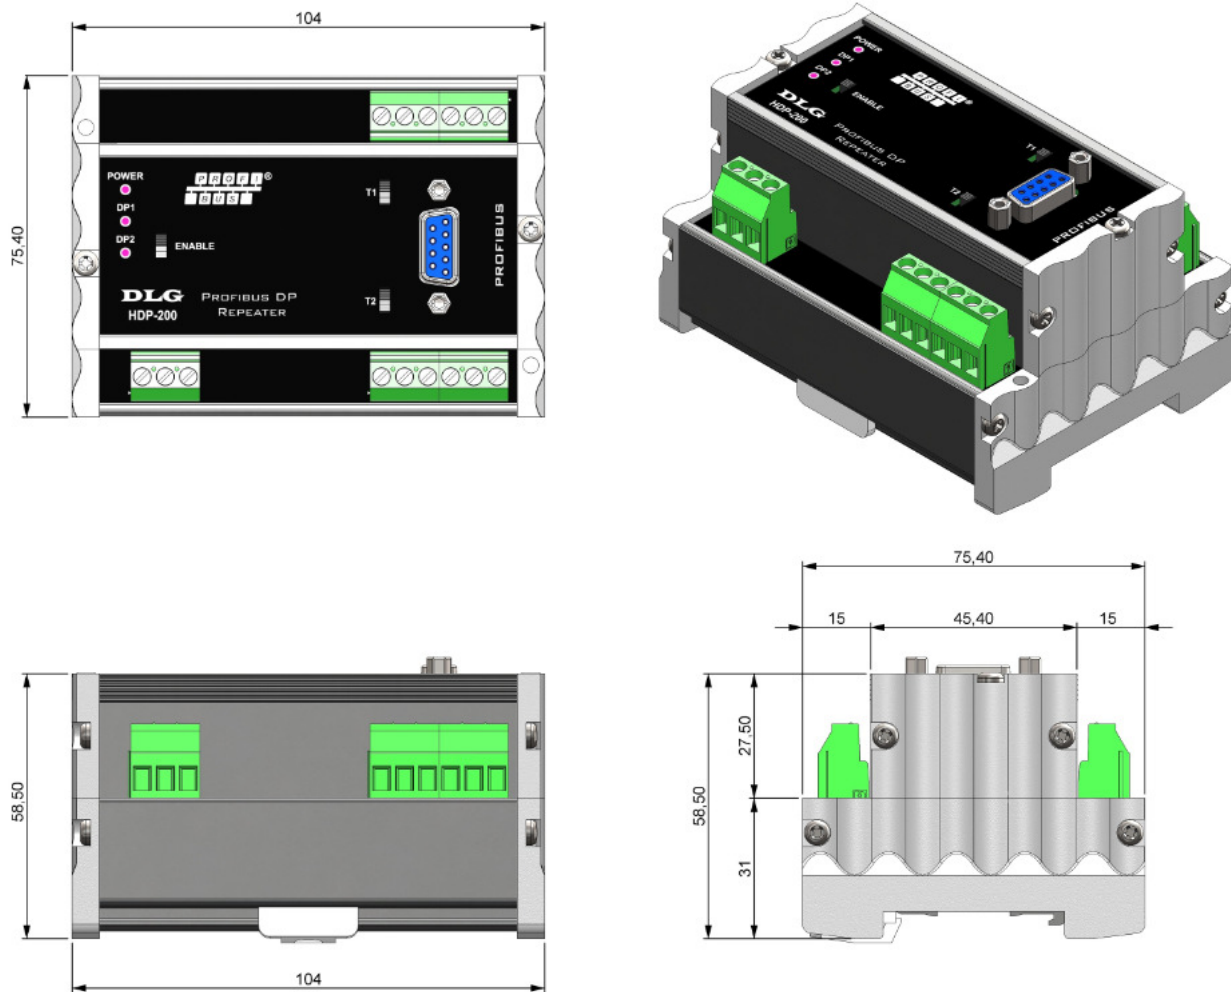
Dimensionamento para montagem (cotas em milímetros)
